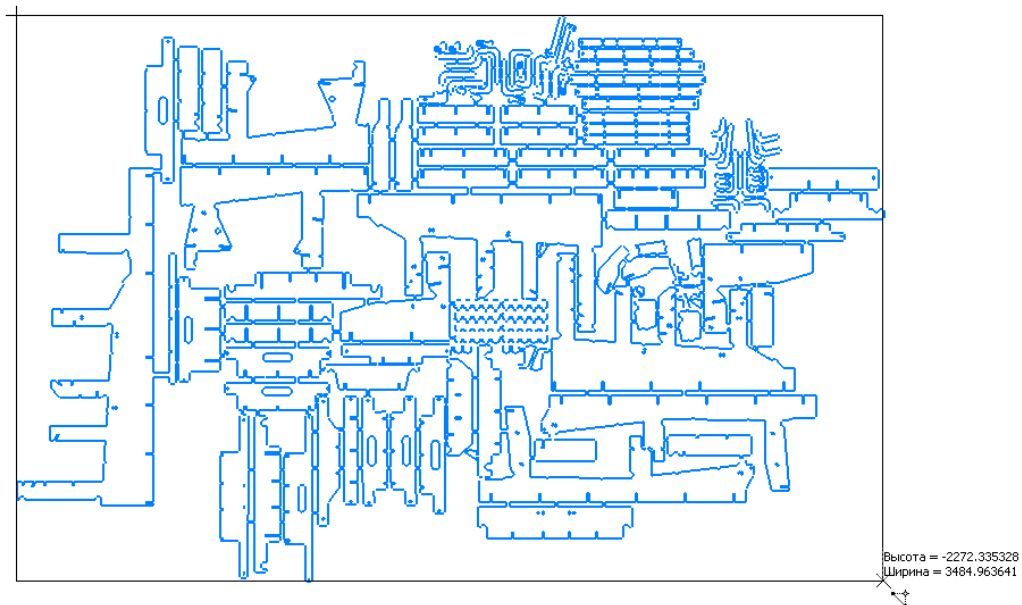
Эскиз деталей для изготовления стапеля на лазерном станке
